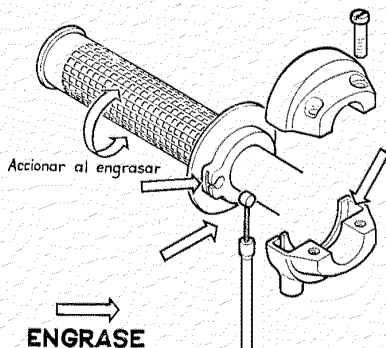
Puño de gas: Engrase y cambio del cable-funda.
